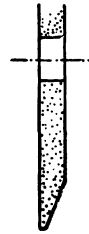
Scheibe für gefräste Fräser mit Abschrägung.
